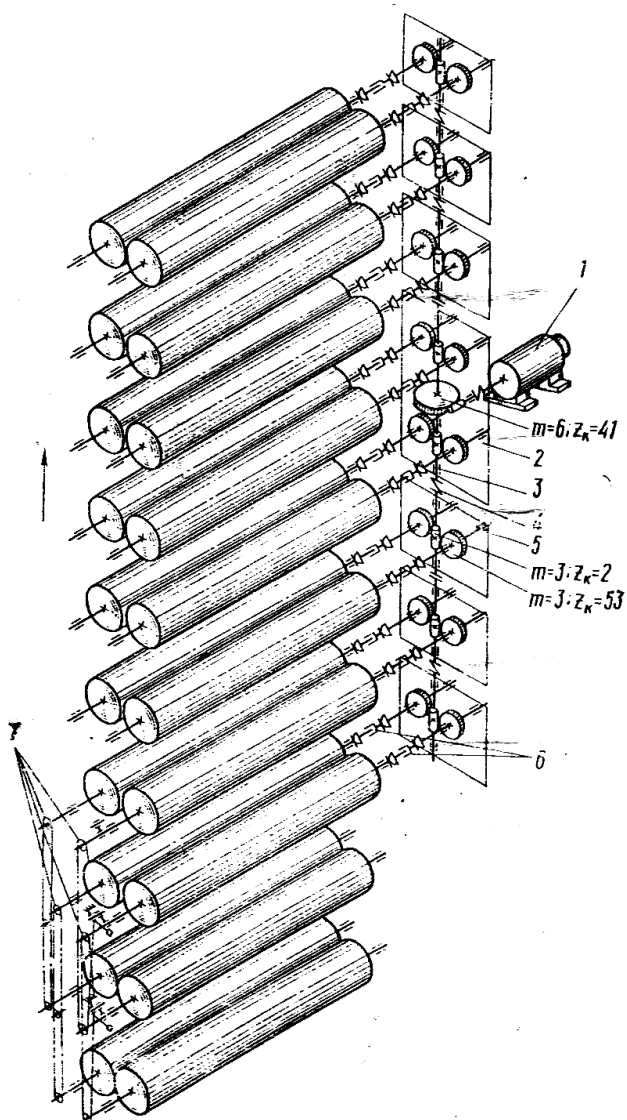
Кінематична схема приводу валиків машини вертикального витягування скла: 1 – електродвигун, 2 – черв'ячний редуктор, 3 – вертикальний вал, 4 – ланцюгові муфти, 5 – черв'ячний редуктор, 6 – карданні валики, 7 – ланцюгові передачі.
